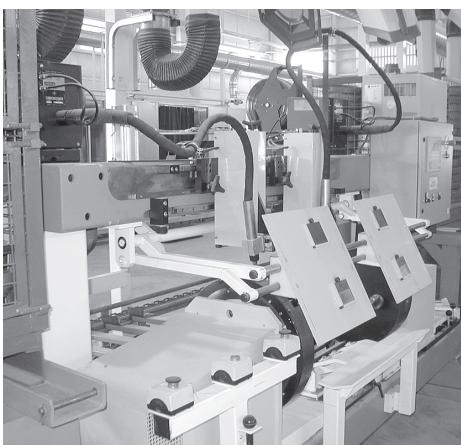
Полуавтоматическое оборудование для поверхностной сварки
